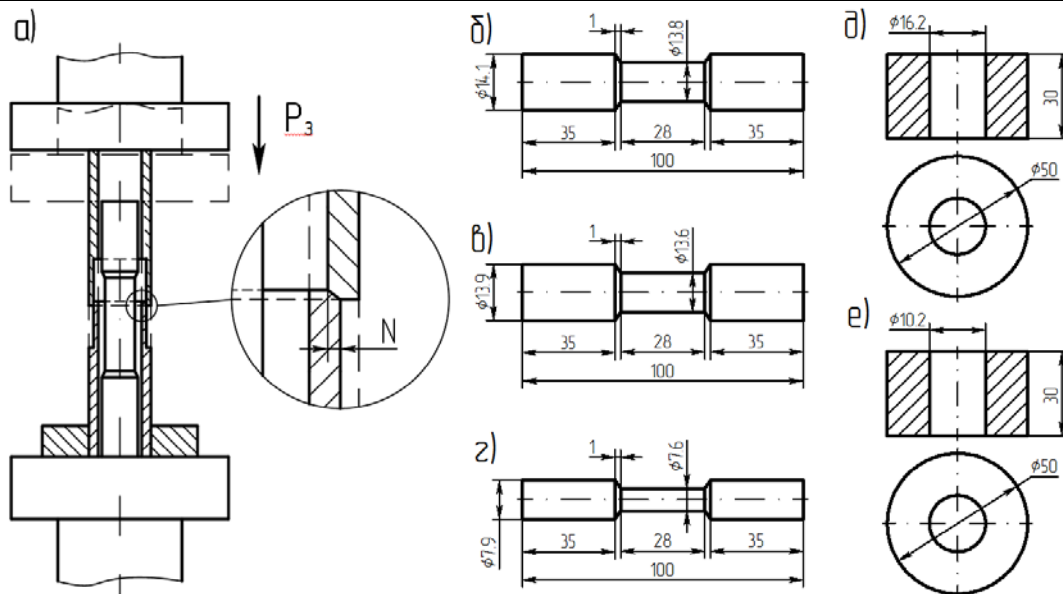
Схема получения прессового соединения: а – схема запрессовки образцов; б – центрирующий штифт для титановых образцов; в – центрирующий штифт для алюминиевых образцов; г – центрирующий штифт для стальных образцов; д – опора для титановых и алюминиевых образцов; е – опора для стальных образцов; $P_з$ – усилие запрессовки; N – величина натяг в соединении
